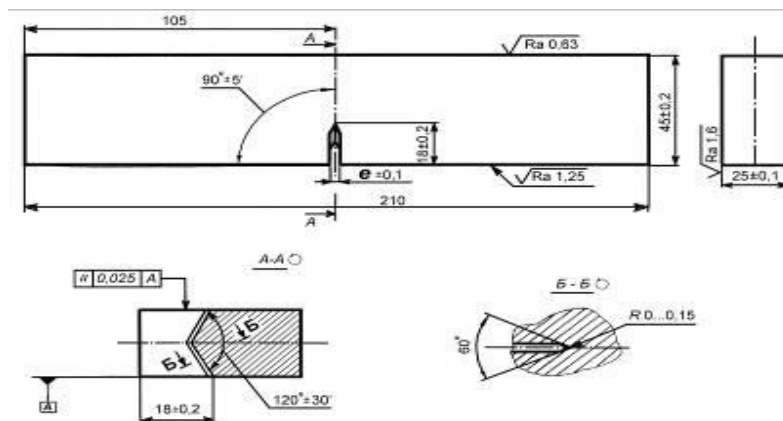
Вид и основные размеры образца для испытаний на статическую трещиностойкость
